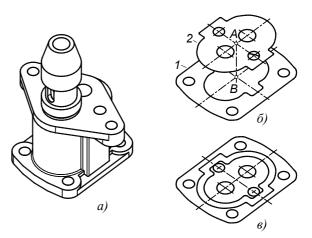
Построение контура основания крышки: a — сопрягаемая деталь — корпус; δ — сечения корпуса; ϵ — совмещение сечений в единую плоскость
